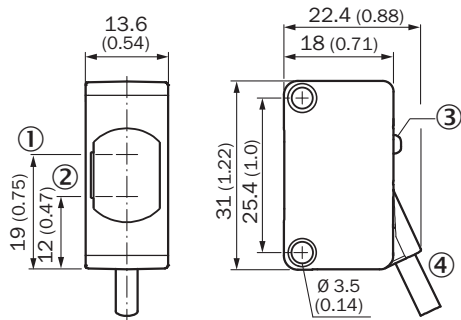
ZLx18-7xxxxx/ZLx18-Gxxxxx, cable
